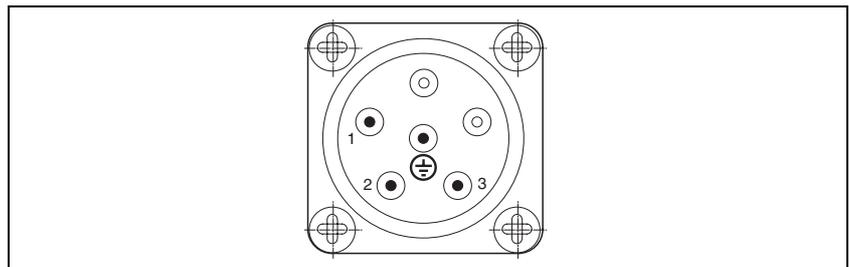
Stecker, Ansicht motorseitig auf die Kontaktstifte
